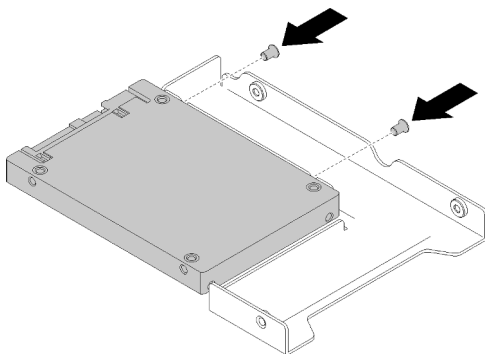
Установка винтов для фиксации твердотельного диска в адаптере для дисков
